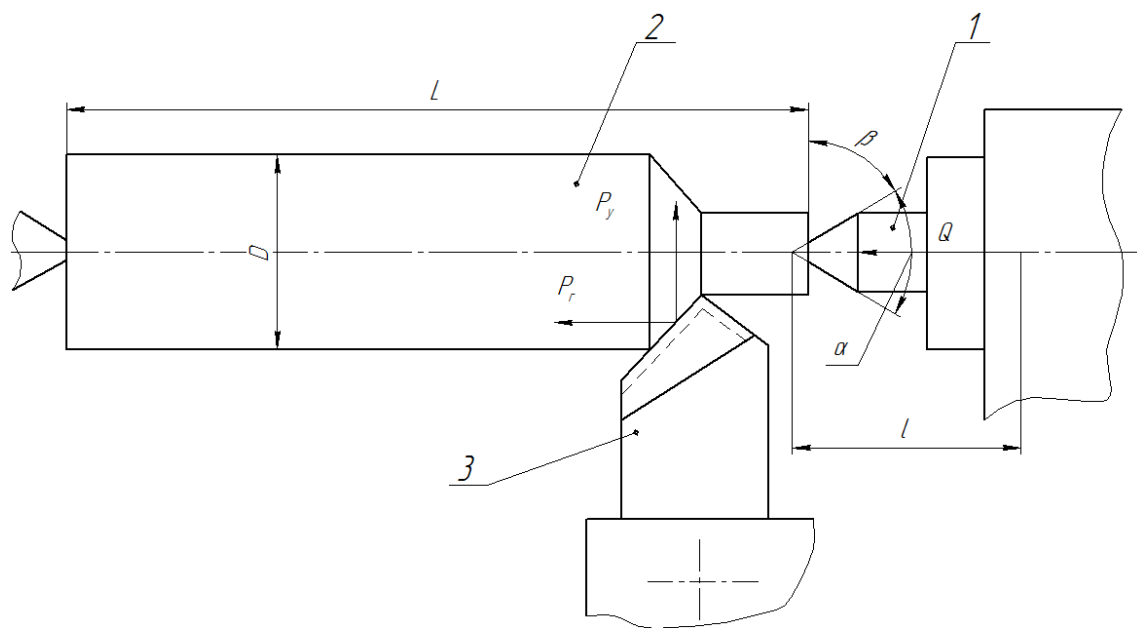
Схема для обчислення зусилля закріплення заготовки з боку задньої бабки верстата: Q – зусилля закріплення; P_x і P_y – складові сили різання; D – діаметр заготовки; L – довжина заготовки; l – довжина вильоту центра задньої бабки; α – кут центрального отвору; 1 – центр; 2 – деталь; 3 – інструмент
